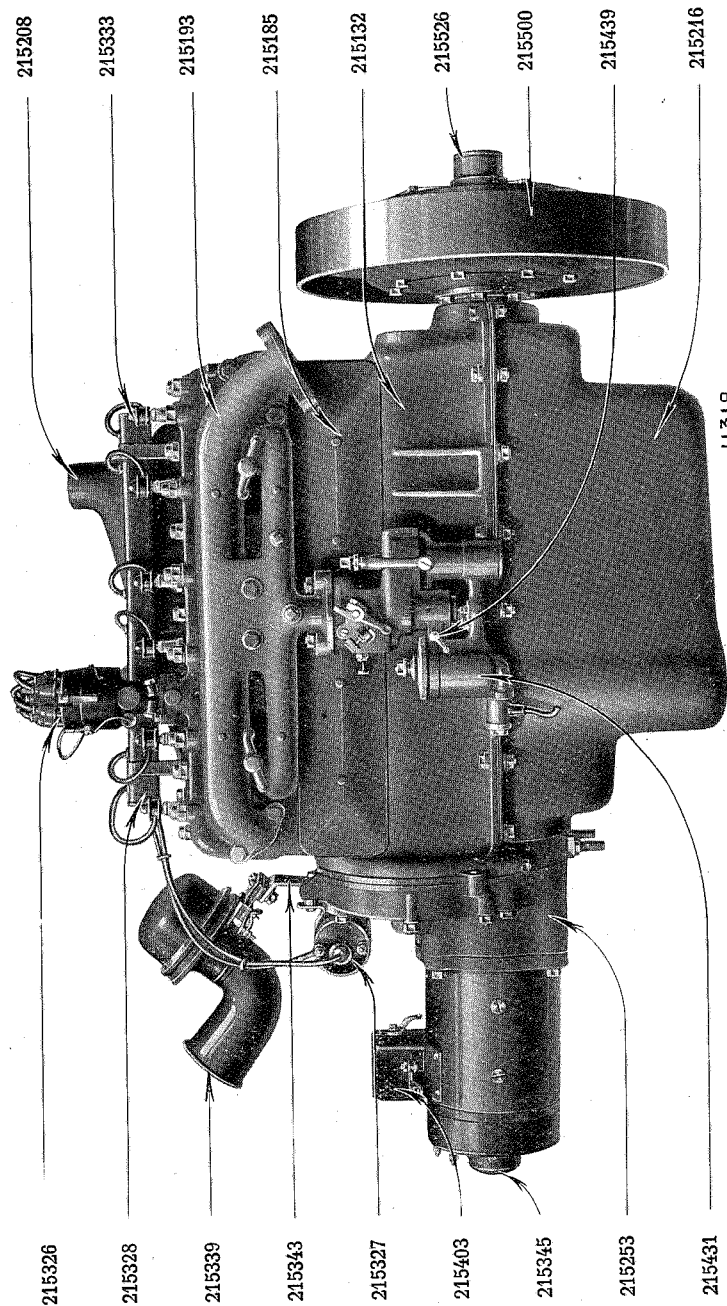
Le moteur. Vue extérieure côté carburateur.
